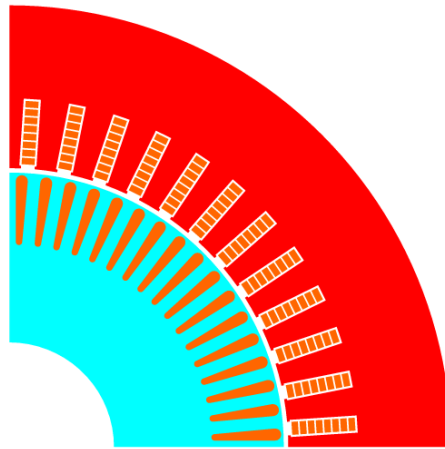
IM con bobinado de estator tipo horquilla [22].
